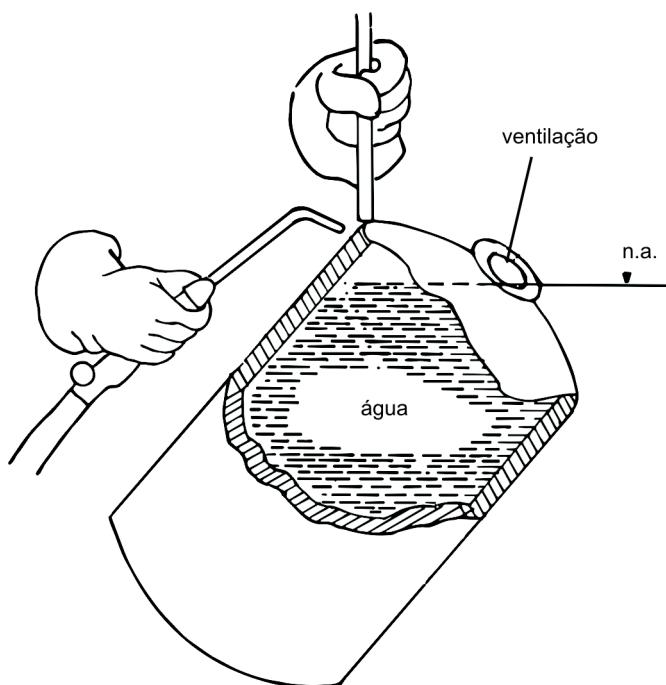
Recipiente Pronto para Soldagem ou Corte
